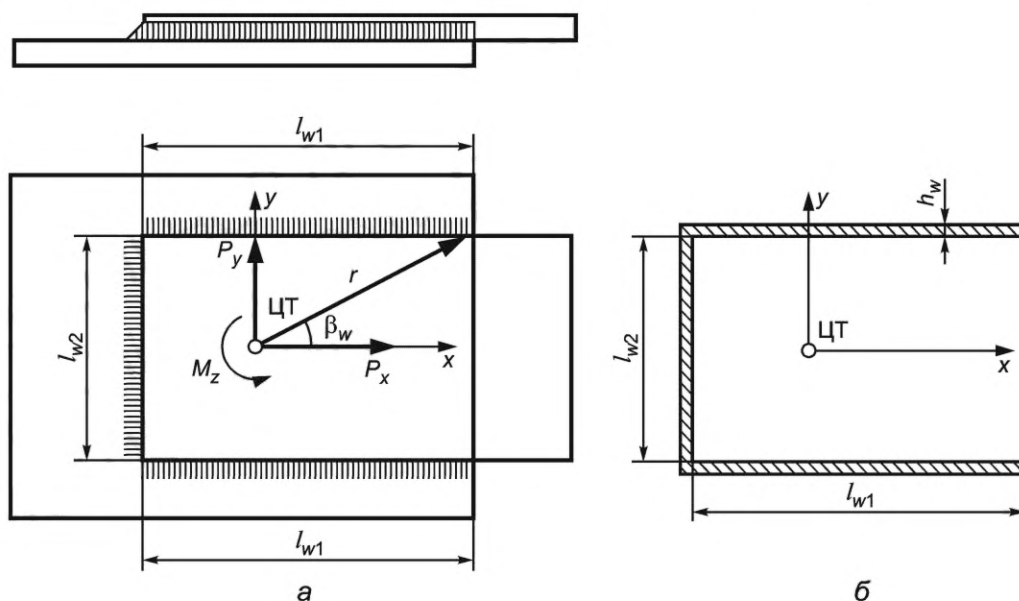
Схема сварного нахлесточного соединения (а) и площадь среза шва (б)
